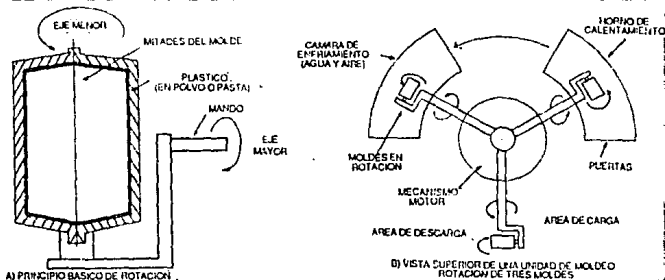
Moldeo rotacional. (Ref. 26).
